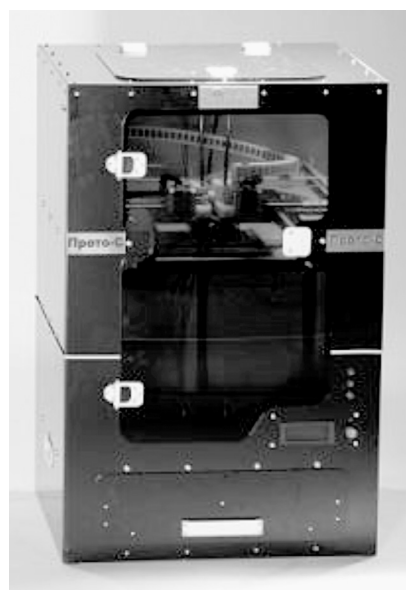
Универсальный 3D-принтер Прото-С (www.proto-s.com)
